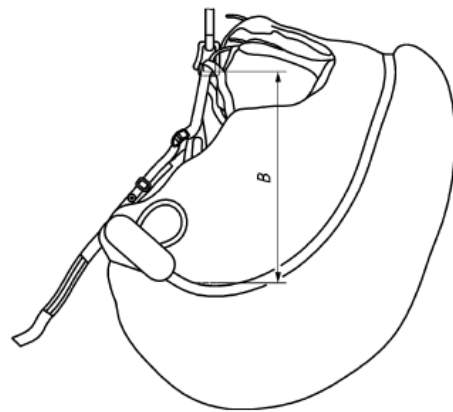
Höhe der Befestigungspunkte des Gurtzeugs
